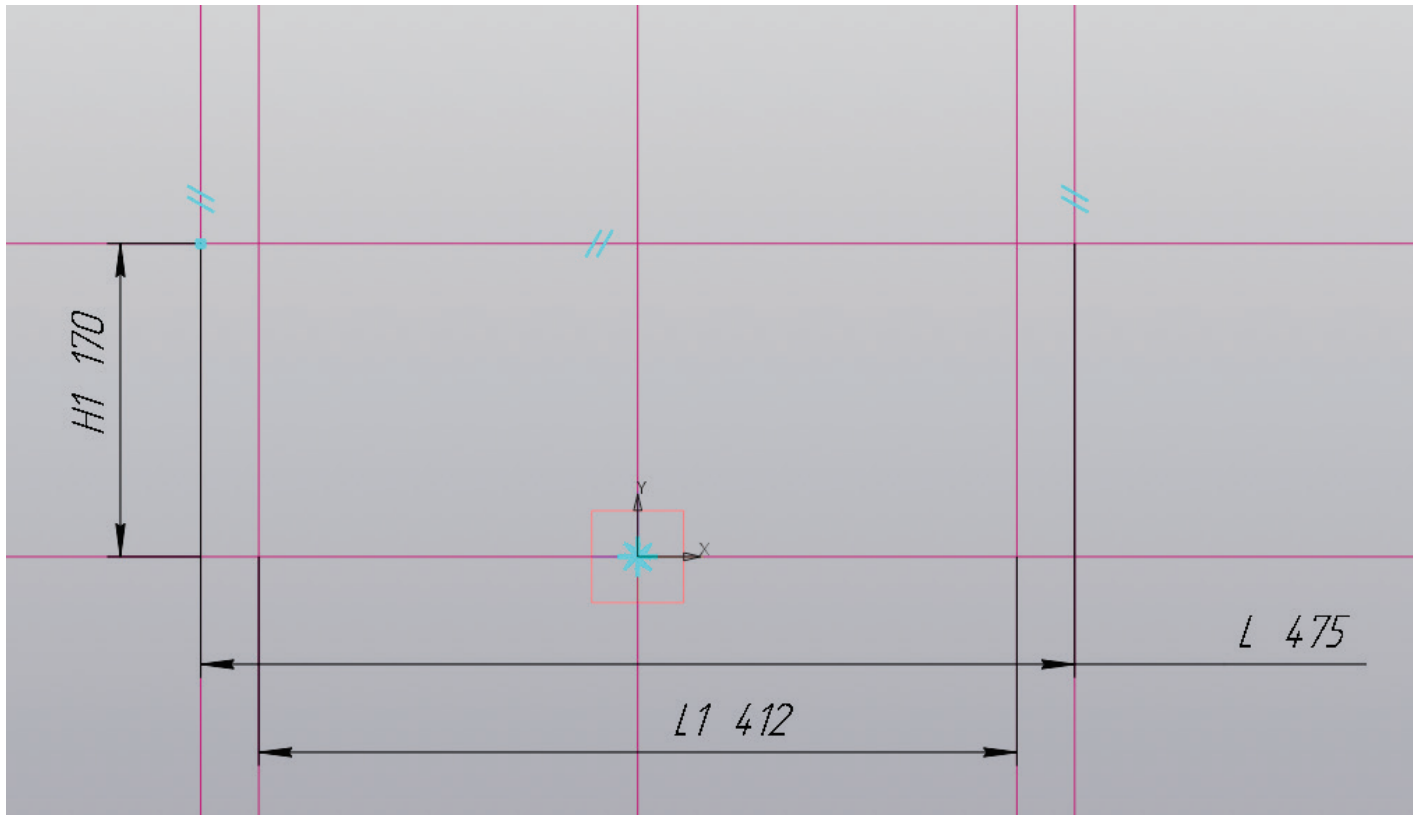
Редуктор цилиндрический, работа с эскизом, вспомогательные прямые
